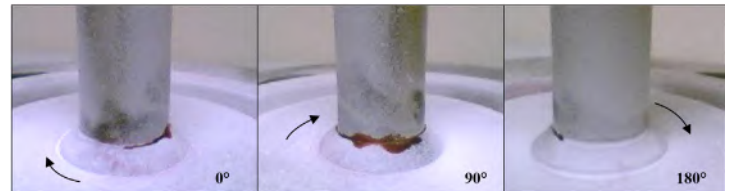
Grieta en el perímetro superior del cordón de soldadura del termopozo
